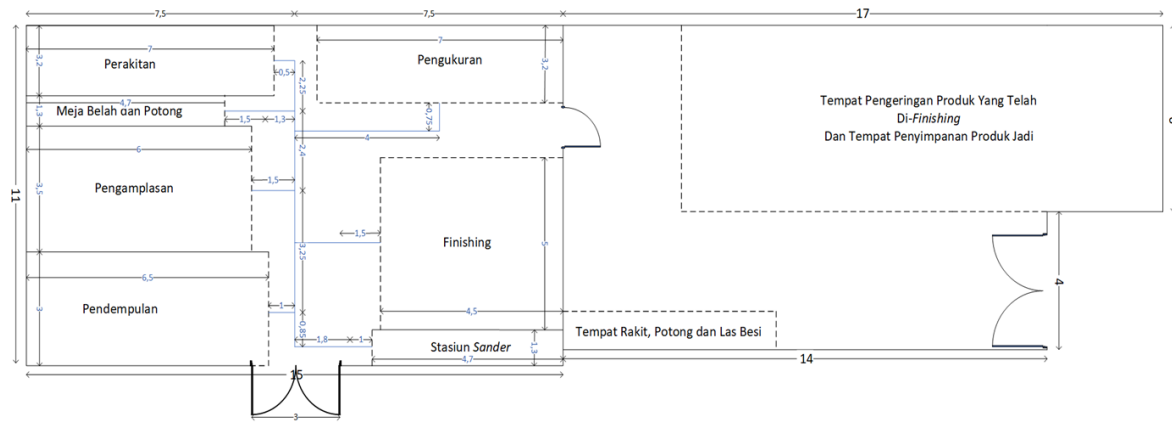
Layout Alernatif 2 UMKM Allwoden Woodworking
